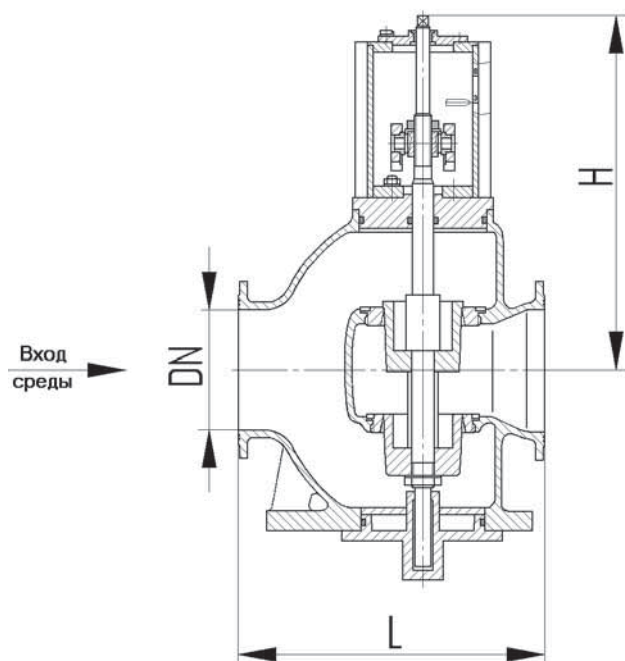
Клапан регулирующий проходной фланцевый
